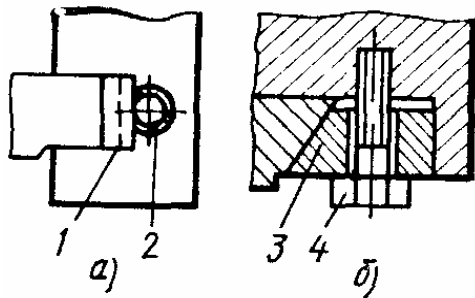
Схеми регулювання зазору в напрямних: 1 – клин; 2 – гвинт; 3 – притискна планка; 4 – кріпильний болт
